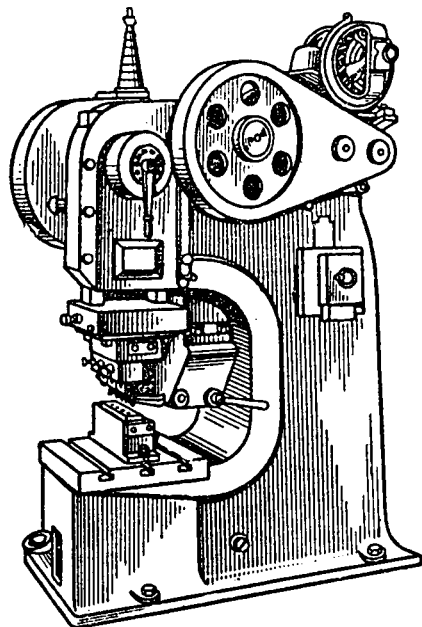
Механический пресс для пробивания отверстий с многштемпельным инструментом
